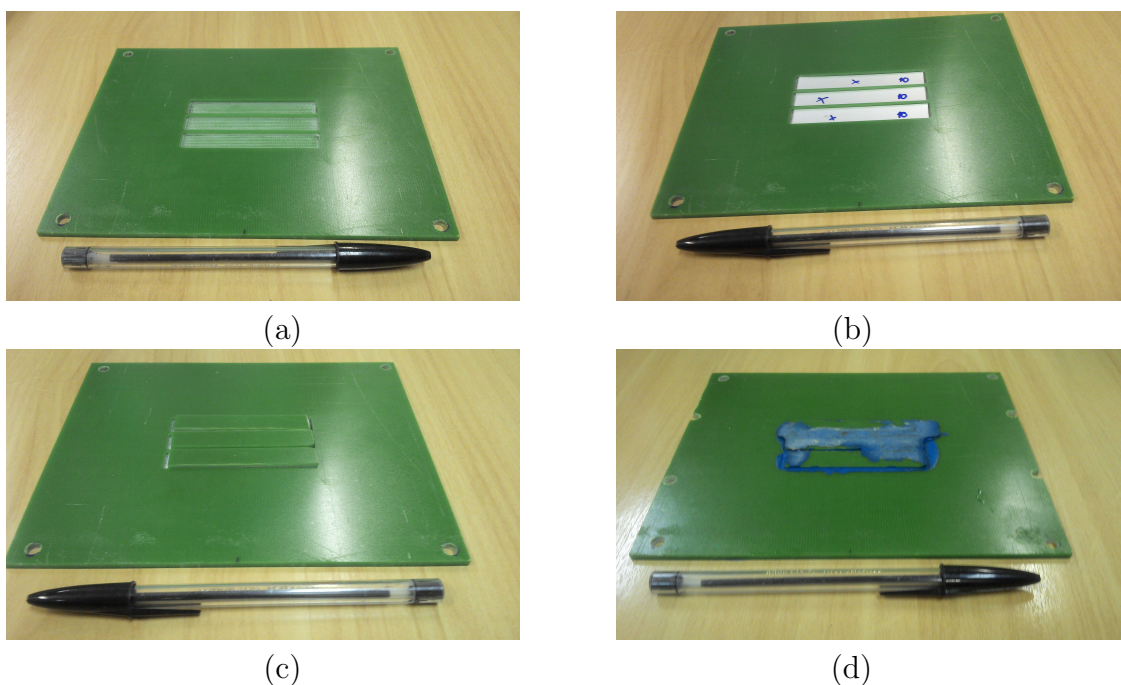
Etapas do processo construtivo da Placa 2G: (a) Placa de G10 com cavidades para colocação dos segmentos de fita 2G, (b) Fitas 2G posicionadas, (c) Tampa de G10 protegendo as fitas e (d) Conjunto resinado.
